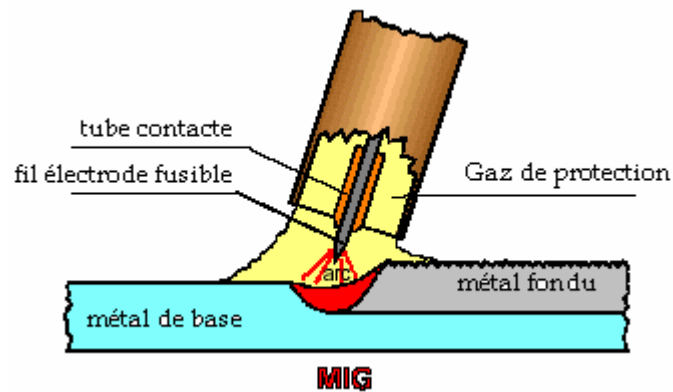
Schéma de principe du soudage MIG
